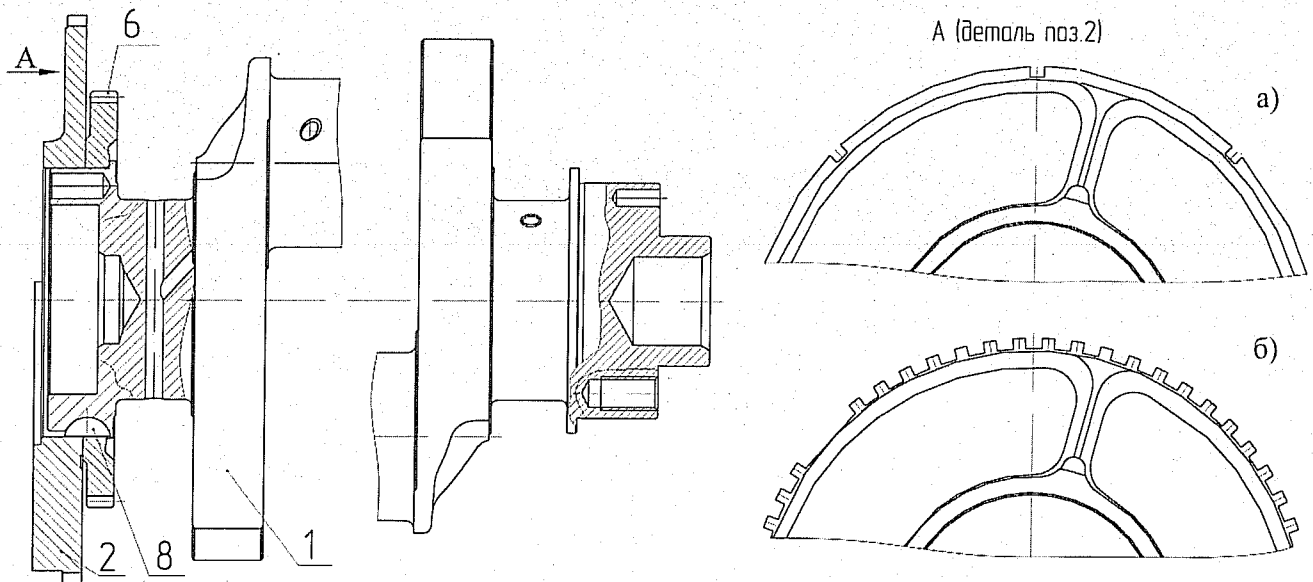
Сборочный чертеж коленчатых валов двигателей уровня Евро-3 с электронной топливной аппаратурой (а), Евро-3 и Евро-4 с ТА¹ «CR»² и газовых двигателей (б), собранных на базе валов 740.70-1005020 и 740.62-1005020.
